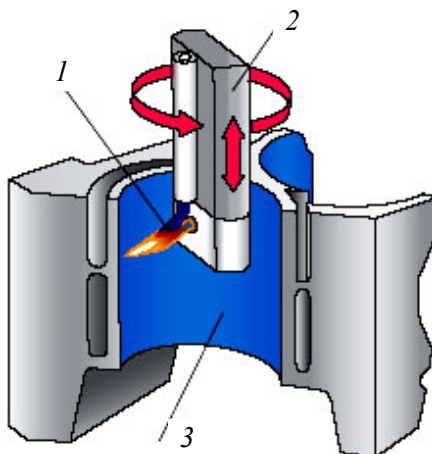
Схема нанесения покрытия на стенки цилиндра плазматроном:
